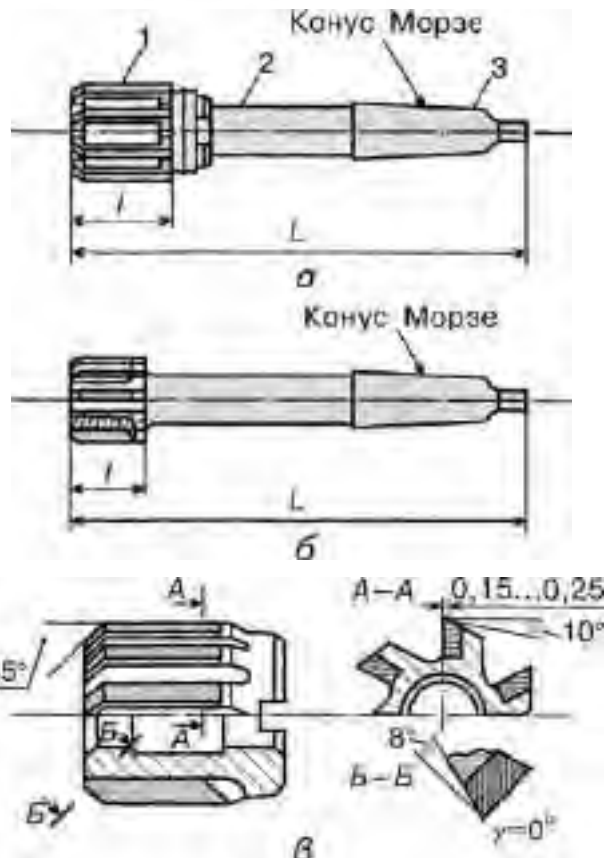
МАШИННІ РОЗВЕРТКИ
